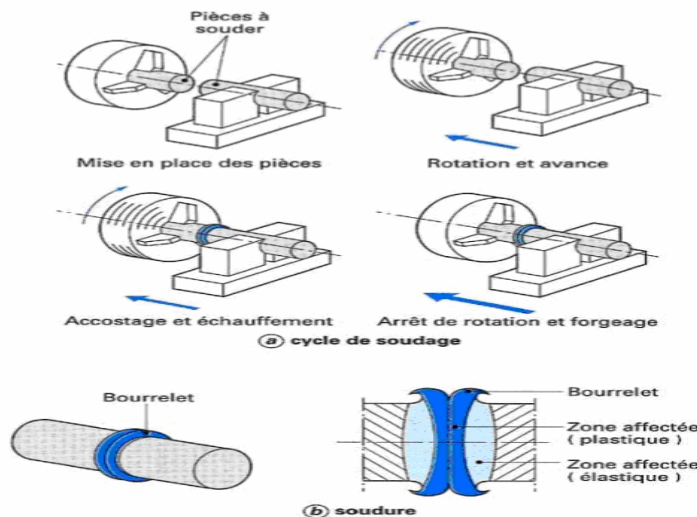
Principe du soudage par friction [11].
